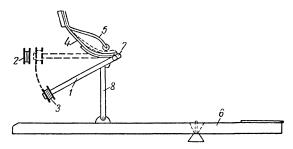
Первый вариалт клавишного трансформатора. I- рычажок; 2 и 3- катушки; 4- пружина; 5- пружинящая пластина; 6-клавиша; 7-шарнир; 8- толкатель;
